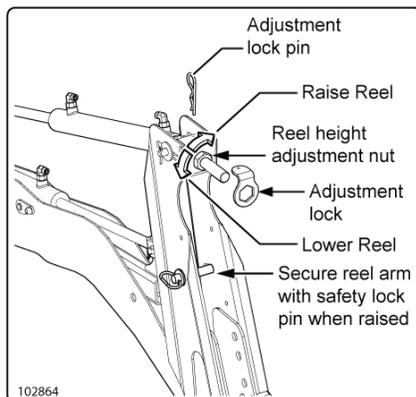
Instructions pour le bras du rabatteur central (Non illustré sur le schéma des autocollants)
